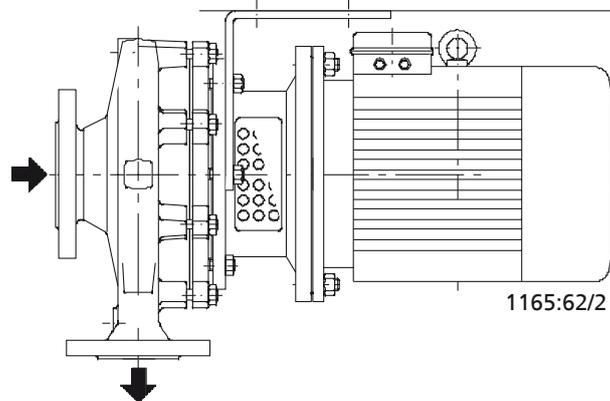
Pumpenfuß Befestigung oben, bis Motorgröße 112 = 4 kW
